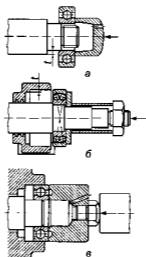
Способы монтажа подшипников: *а* – на вал; *б* – в корпус; *в* – на вал и в корпус одновременно; *t* – размер упорного бурта
